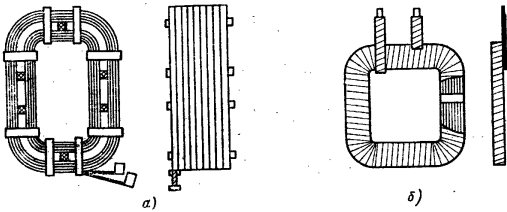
Первичные обмотки сварочных трансформаторов: а — цилиндрическая; б — дисковая
